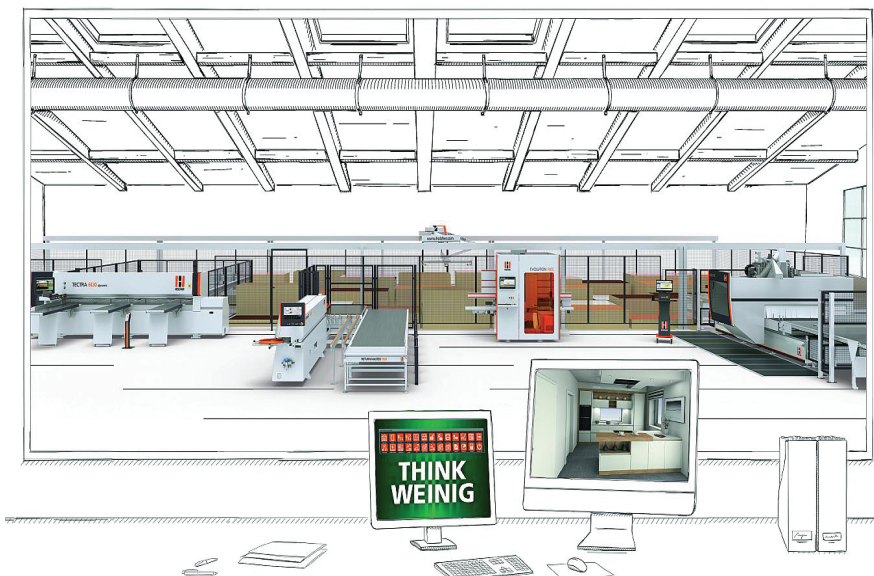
NEXTEC 7735 — универсальный обрабатывающий центр с ЧПУ
